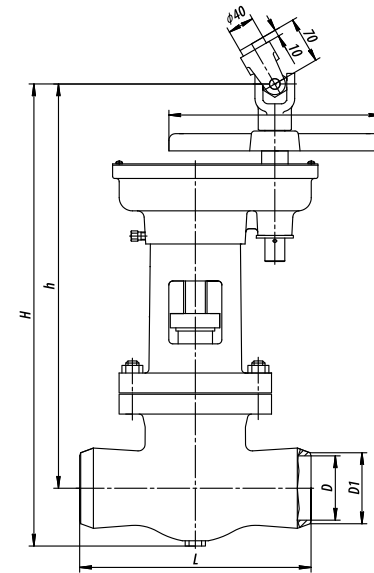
Задвижка DN80-100 с цилиндрическим редуктором
